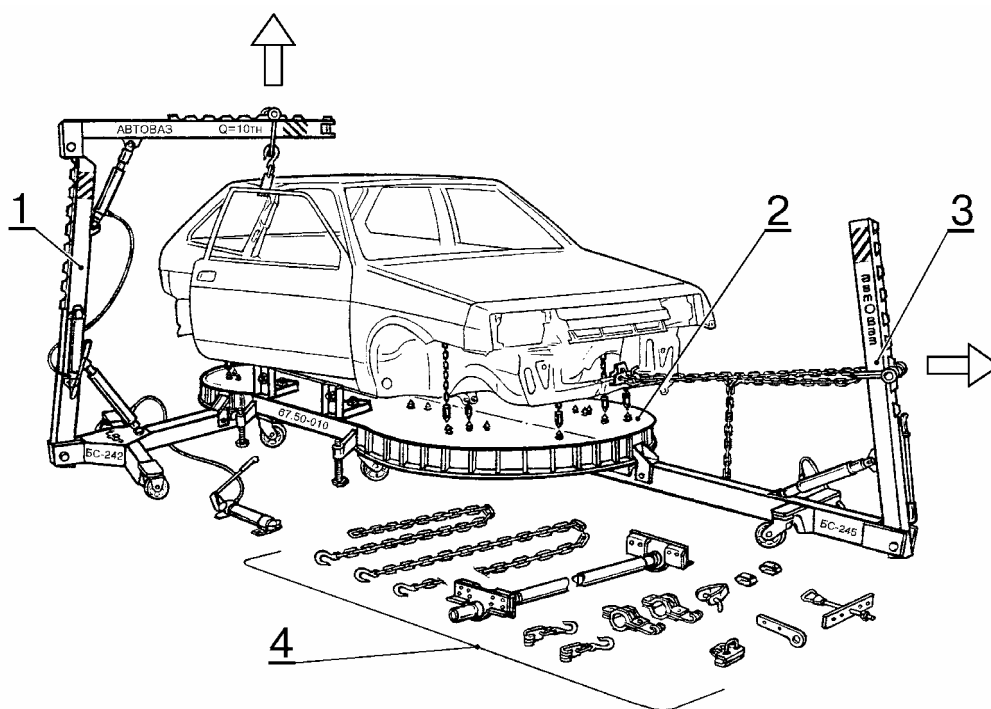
Стенд универсальный для правки кузовов автомобилей ВАЗ (чертеж 67.50.010):
